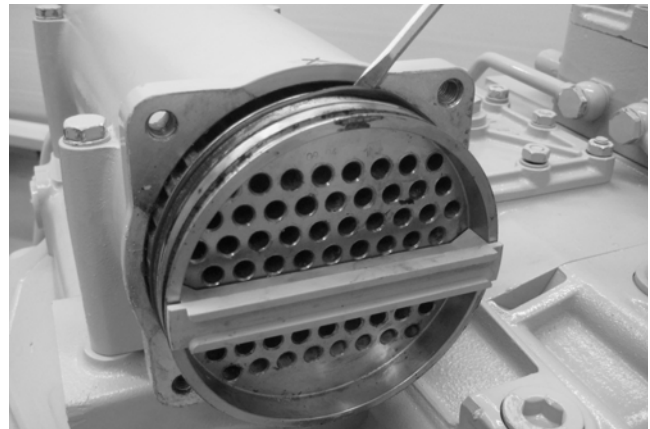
Demontage des inneren O-Rings (Beispiel)
